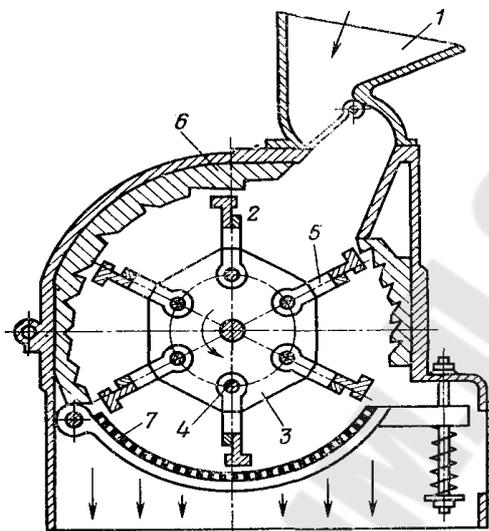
Схема молотковой дробилки: 1- загрузка материала; 2- рабочее пространство; 3- диски; 4- болты; 5- била (молотки); 6- стальная облицовка; 7- решетка
